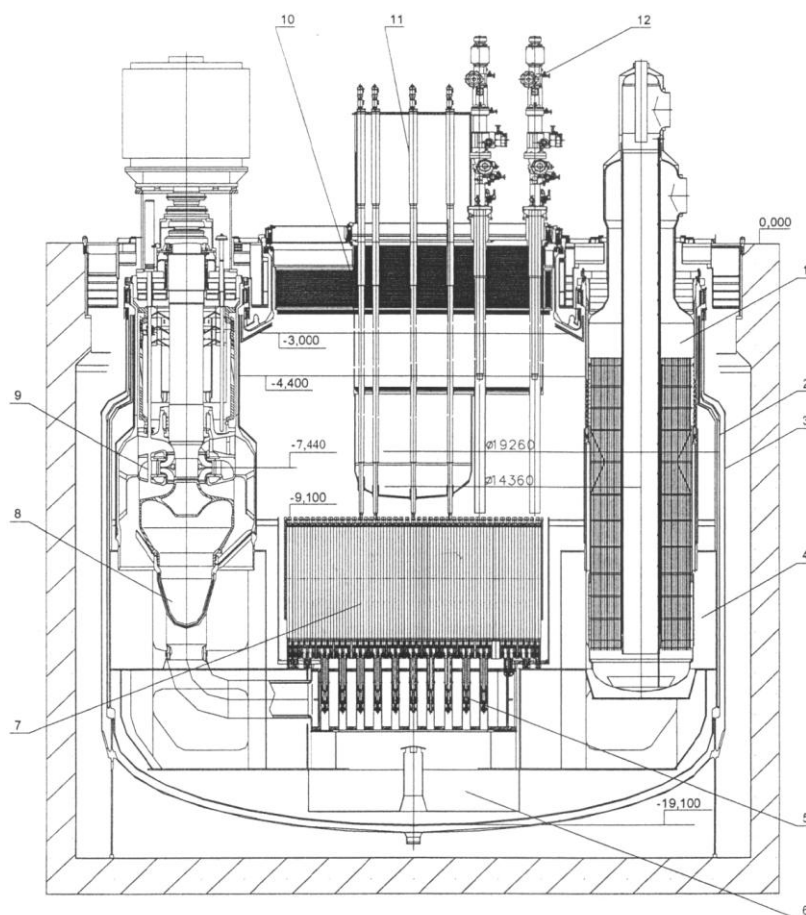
Разрез ГЦН-ПТО реактора БН-1200. 1 – промежуточный теплообменник; 2 – Основной корпус; 3 – Страховочный корпус; 4 – опорный пояс; 5 – напорная камера; 6 – устройство сбора топлива; 7 – активная зона; 8 – на-
